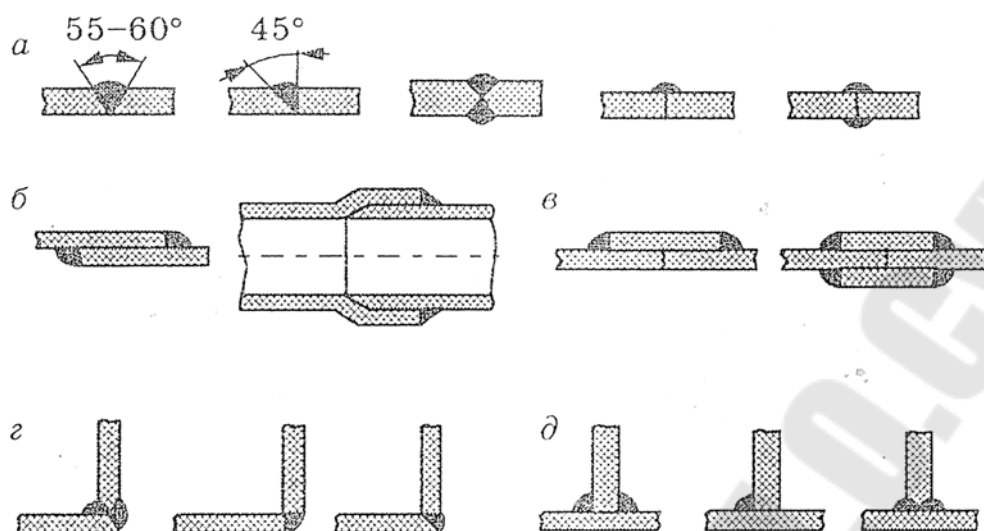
Основные типы сварных соединений полимерных заготовок:
